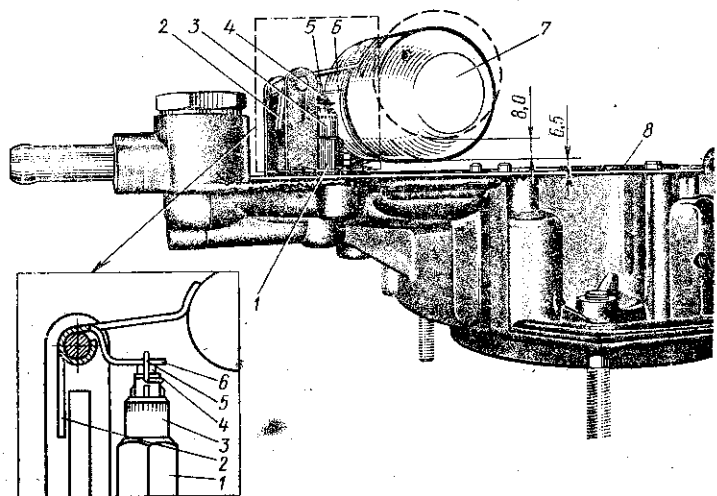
Отрегулированное положение поплавка на крышке поплавковой камеры карбюратора 2101-1107010-11:
